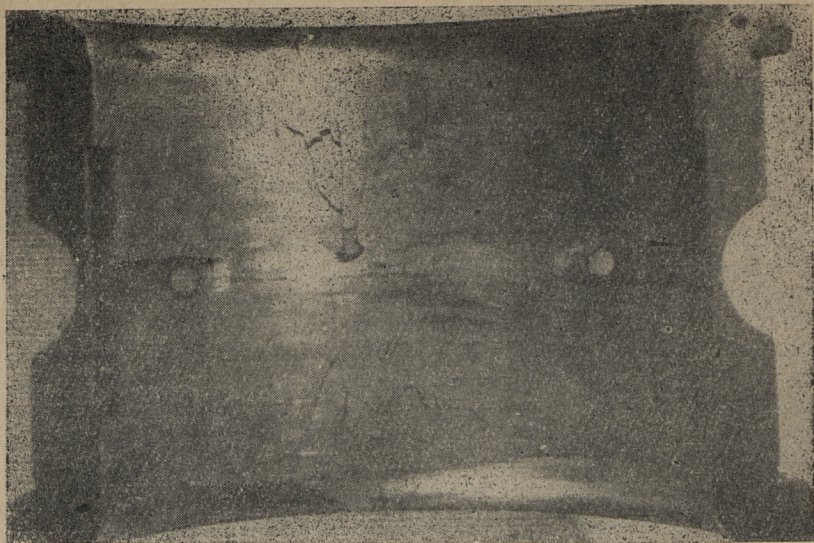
Нижний вкладыш рамового подшипника двигателя 4NVD24 СРТР-9109 (1000 часов работы; баббит Б83)
